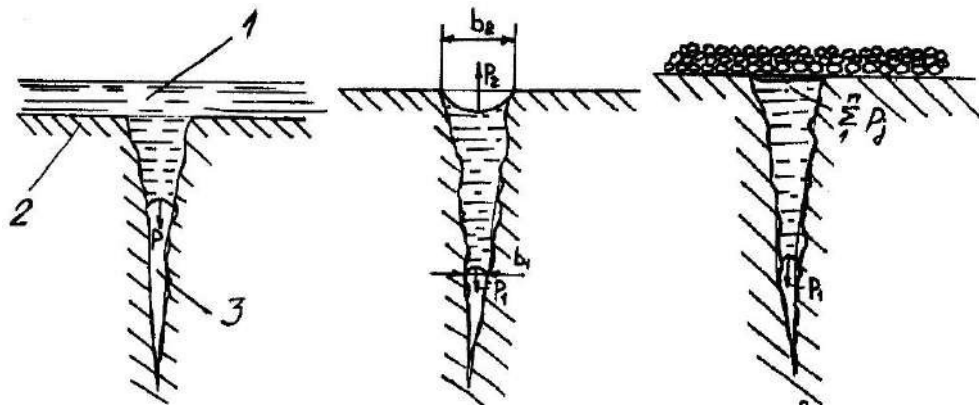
Заповнення рідиною 1 порожнини тріщини 3 на поверхні деталі 2:
